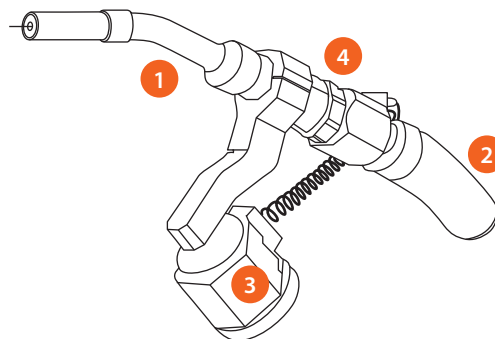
Горелка A7 MIG Gun 500-w
